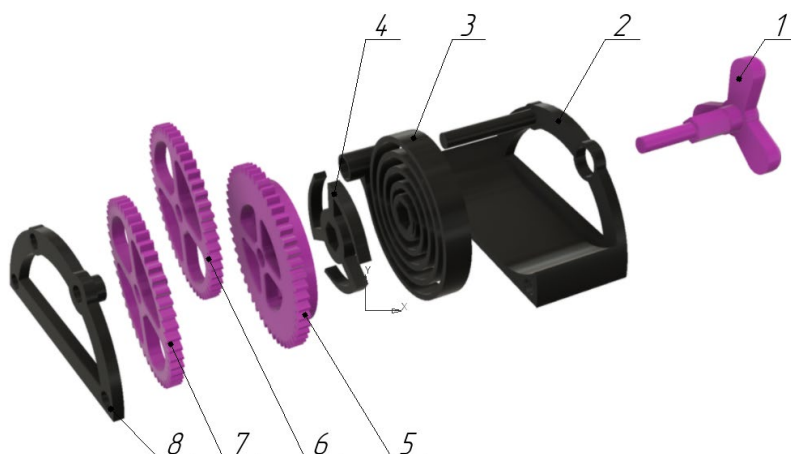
Детализованная схема двигателя с пружинным механизмом
